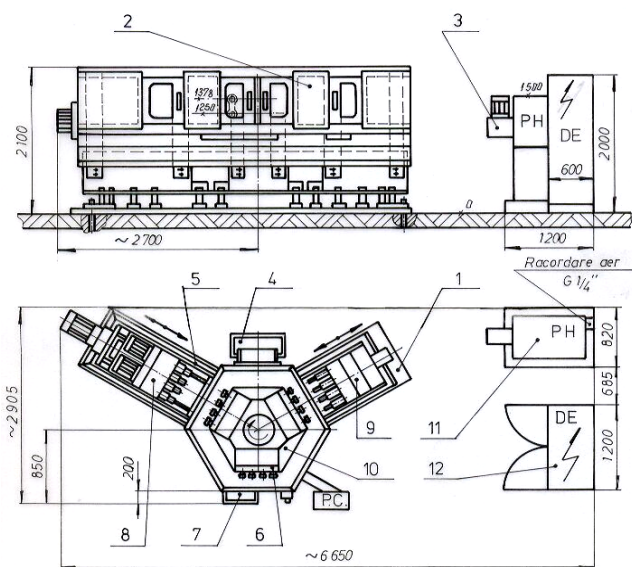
Mașina-unealtă specială de alezat bielă asamblată.
